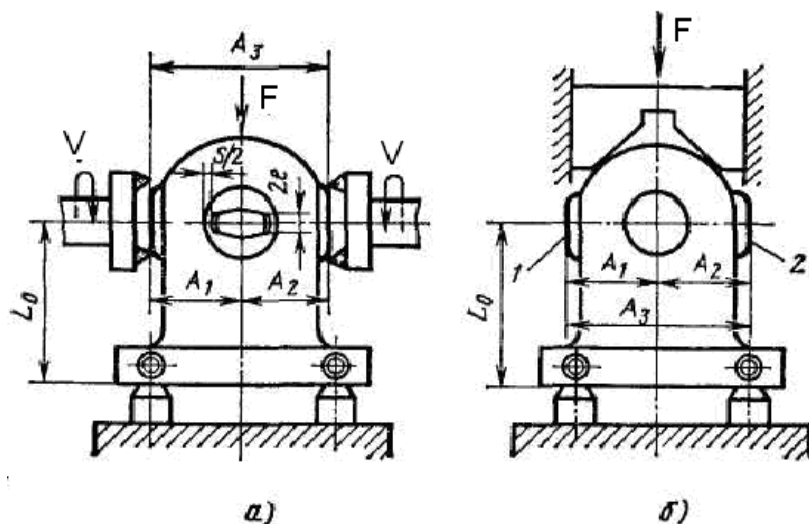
Схеми обробки поверхонь корпусу (до задачі 1.14)
